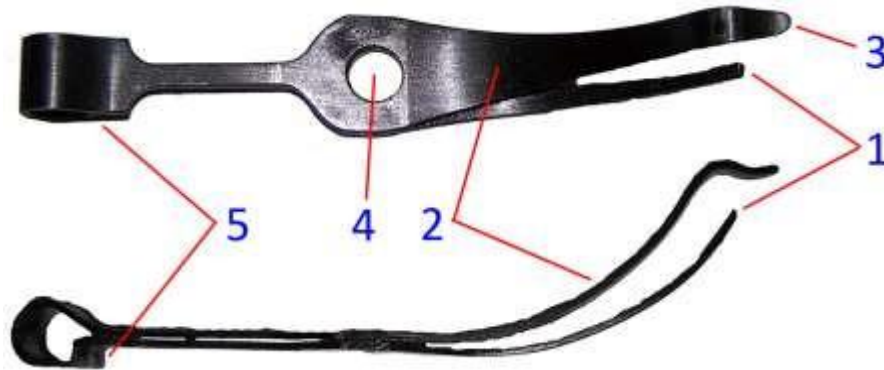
Бойова пружина (вигляд з торця і вигляд з боку):
